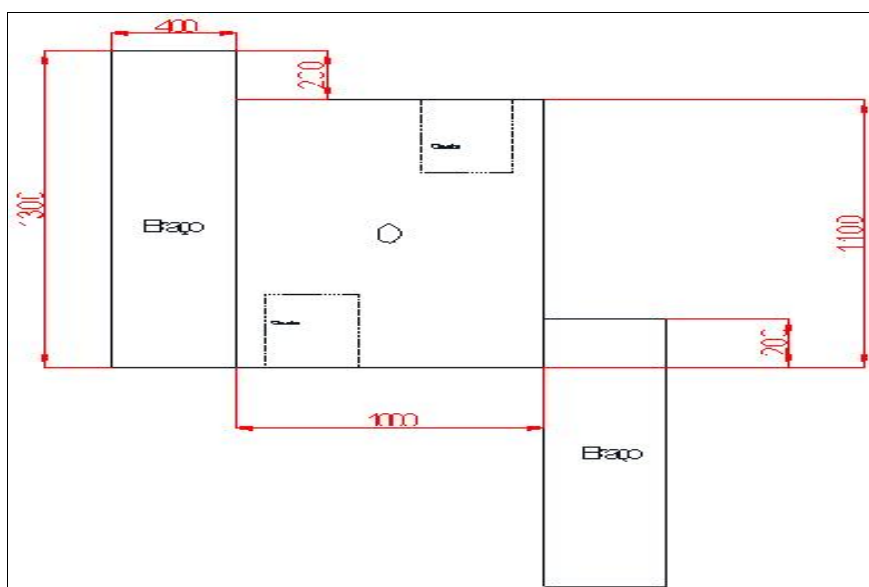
Planta baixa da bancada elevada com valores em milímetros
